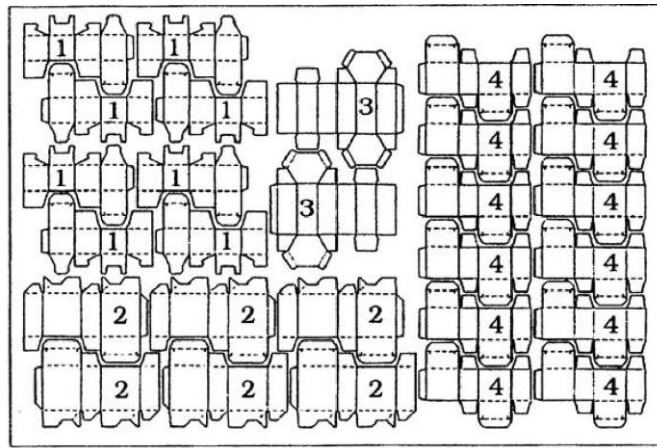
Позичуванням розгорток килькох коробок на форматі заготовки з картону
